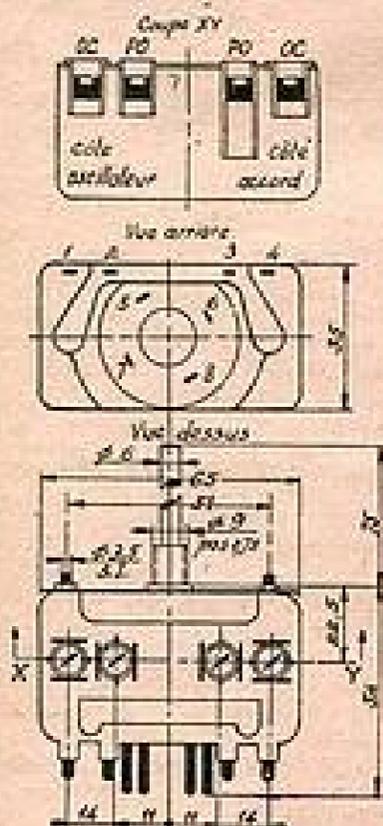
Aspect d'un bloc à 2 gammes : côtes d'encadrement et de perçage pour le châssis, vues arrière, de-dessus et en coupe (Dau-phin Omega)
